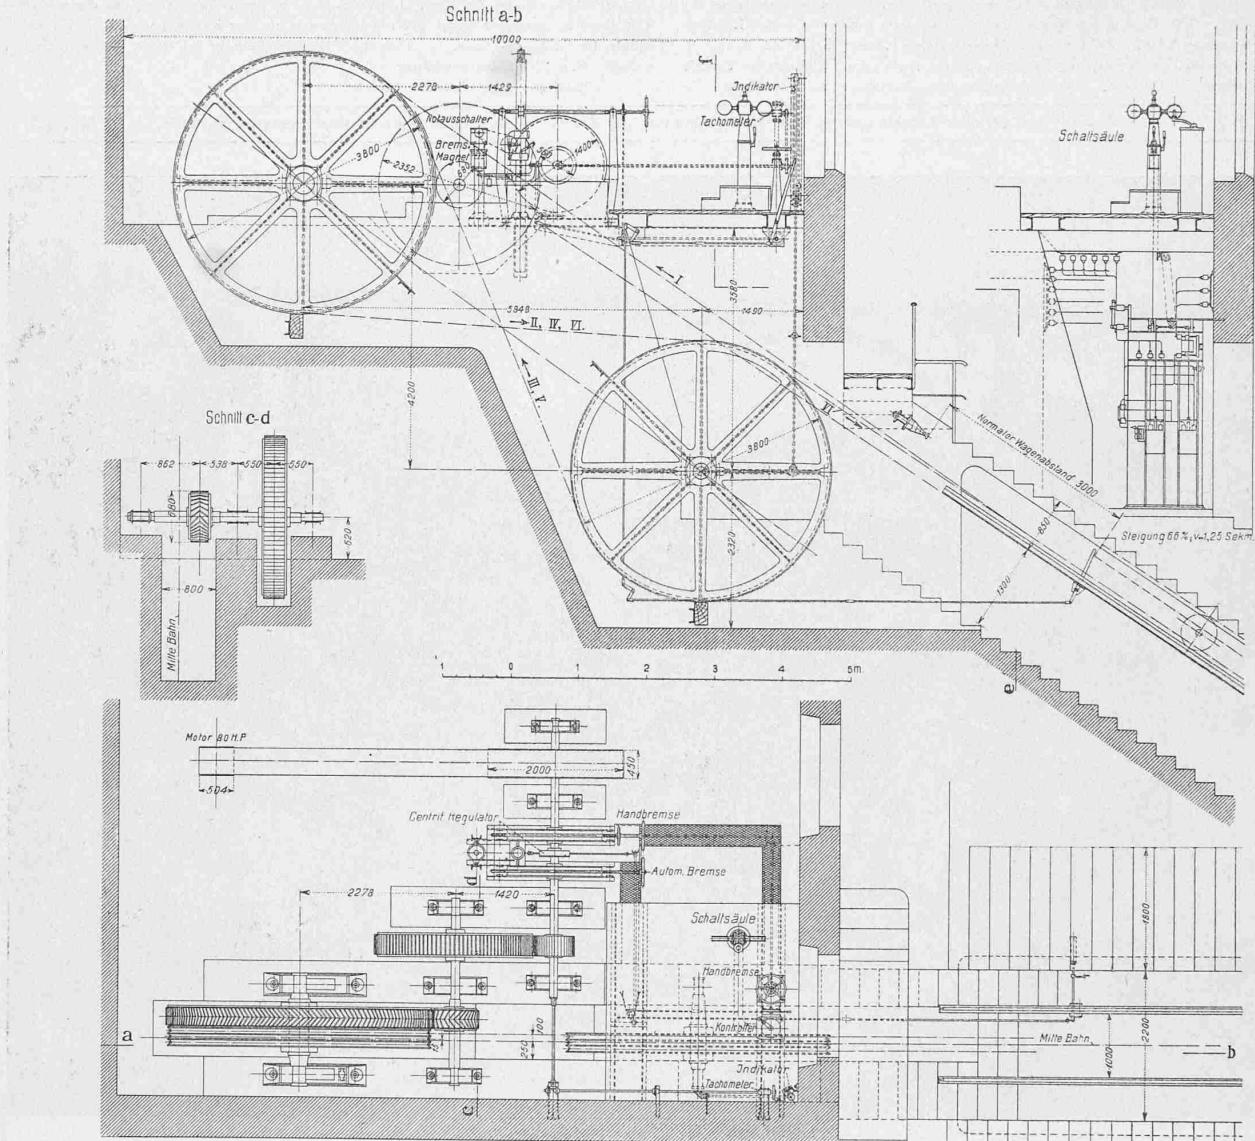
Windwerk der I. Sektion auf der Antriebsstation Schwandegg. — Grundriss und Schnitte. — Maßstab 1 : 100.
